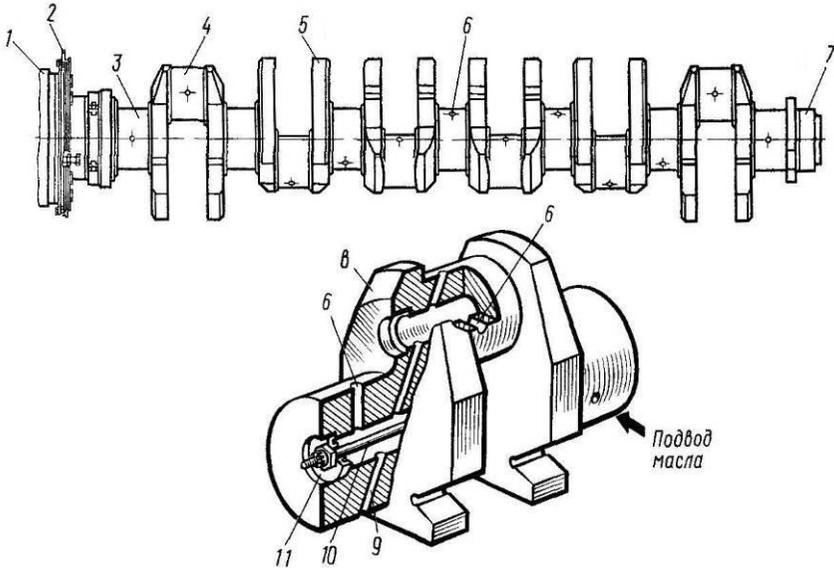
Коленчатый вал дизеля ПД1М
